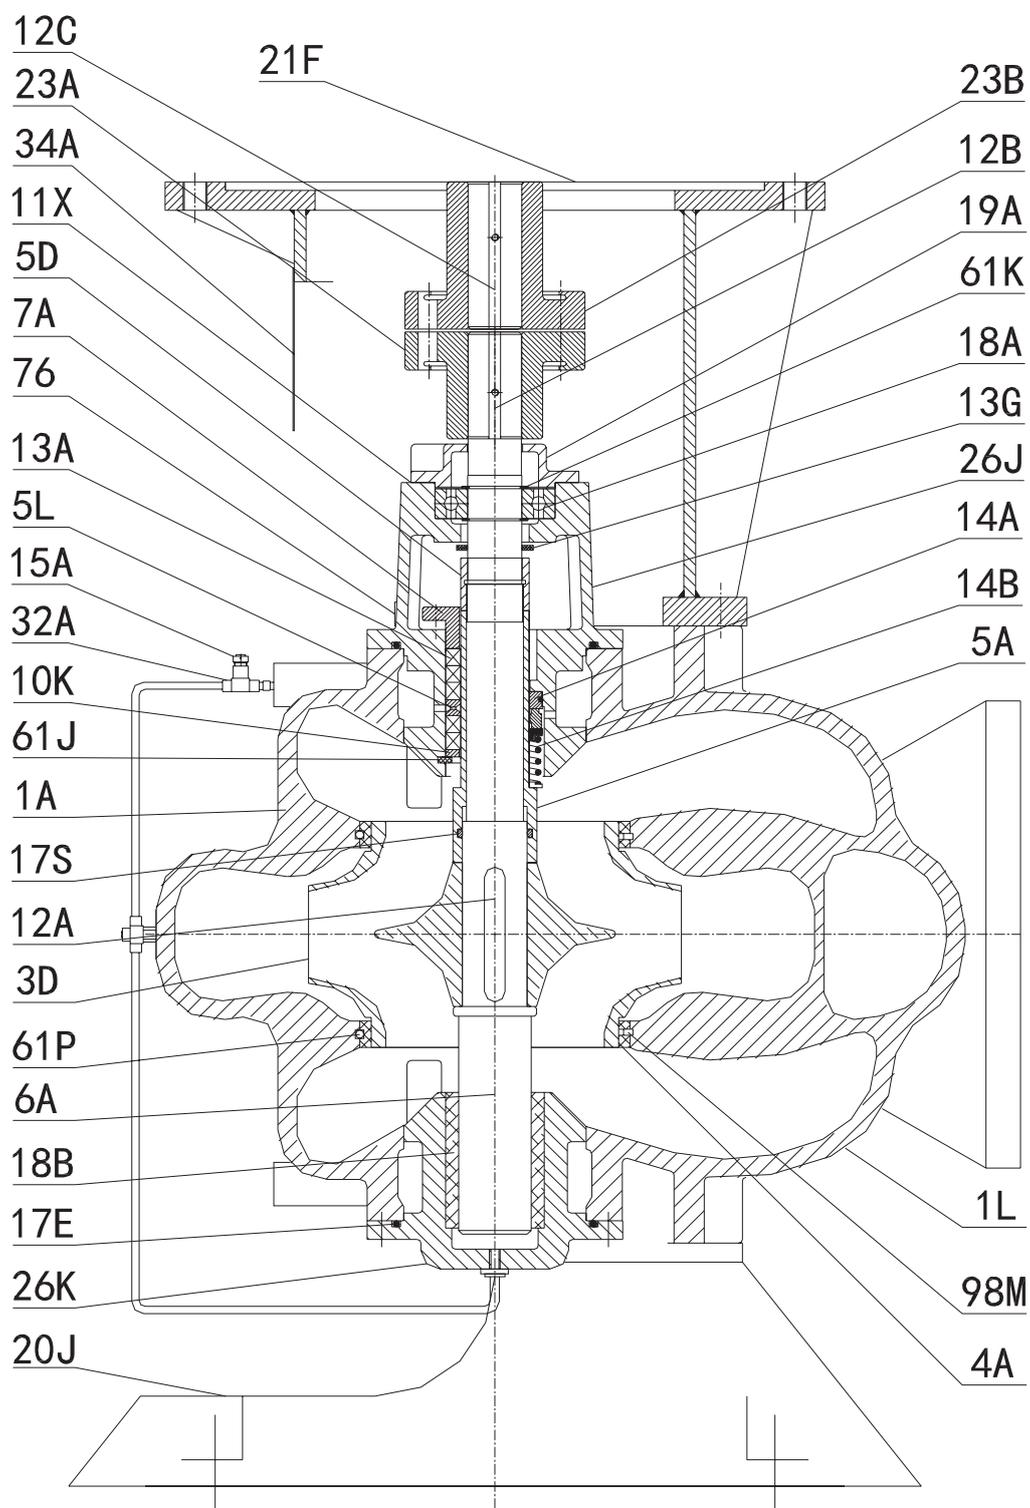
Типоразмер двигателя до 250 кВт включительно
